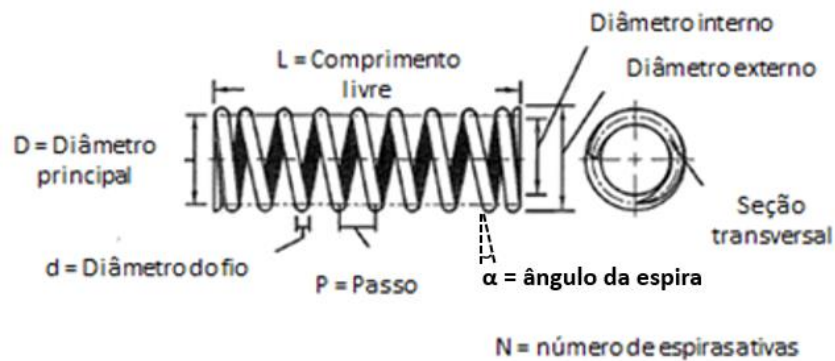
Nomenclatura para mola helicoidal. Adaptado de Milliken e Milliken (1995).
